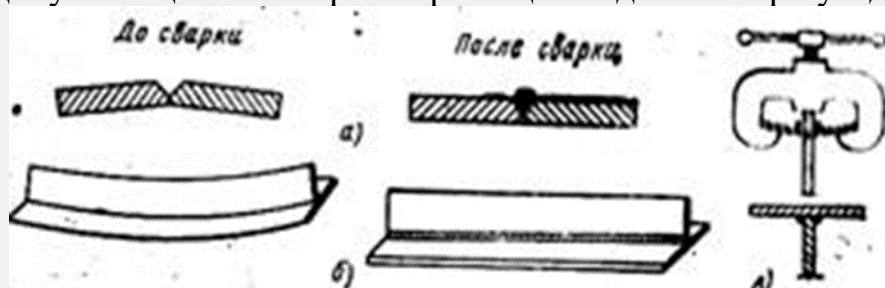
Обратные деформации и положения элементов изделия после сварки А – стыковое соединение двух пластин, б- тавровая балка, в – полка таврового соединения
